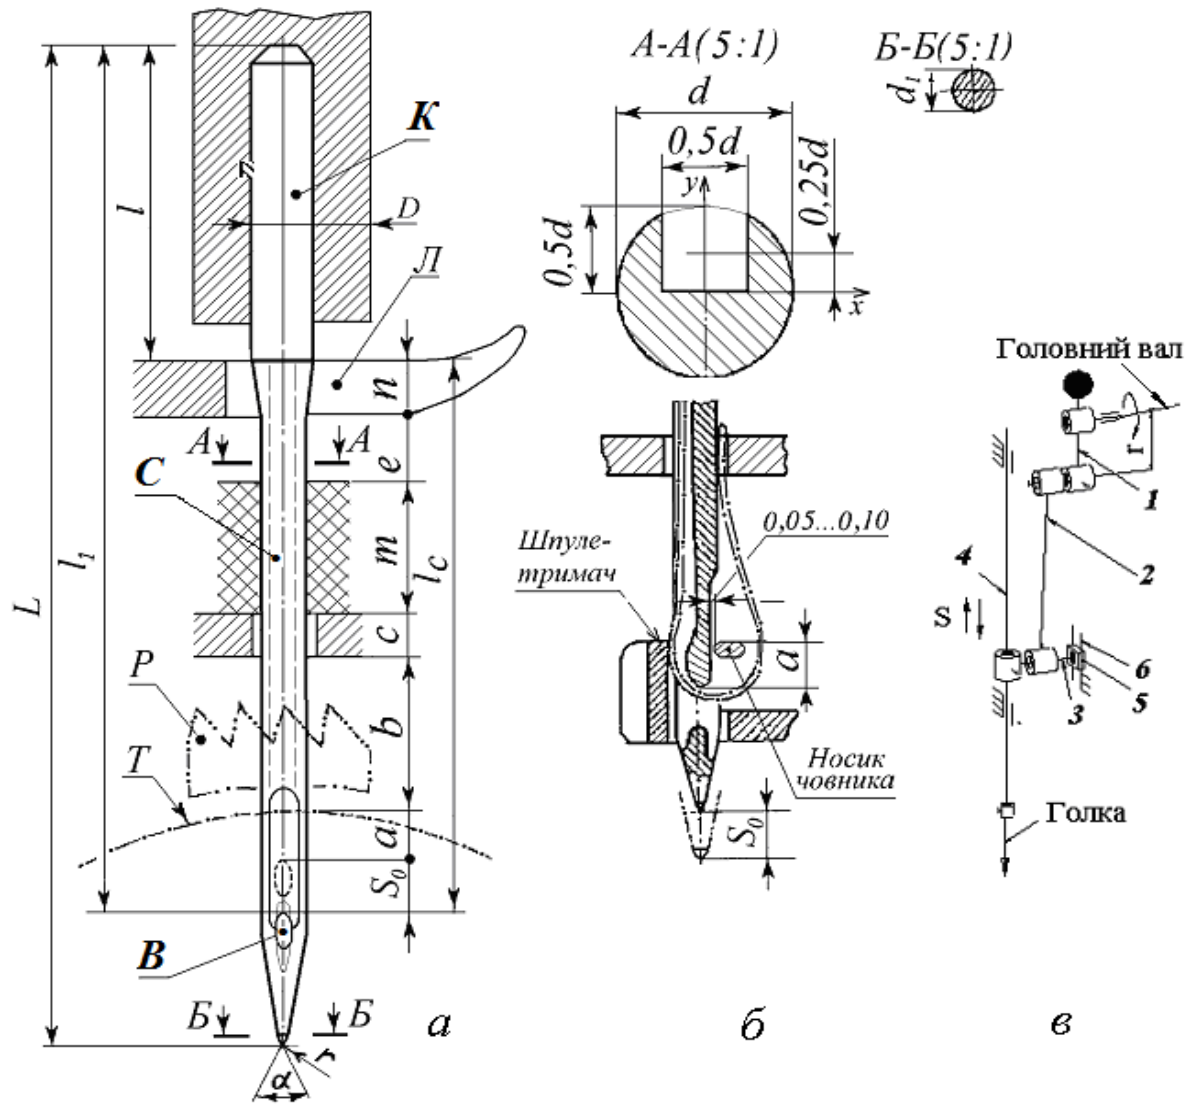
Конструкція голки швейної машини човникового стібка і механізм голки : а– розрахункова схема; б– параметри взаємодії голки з човником; в – кінематична 3D-схема механізму кривошипно-повзунного механізму голки.
